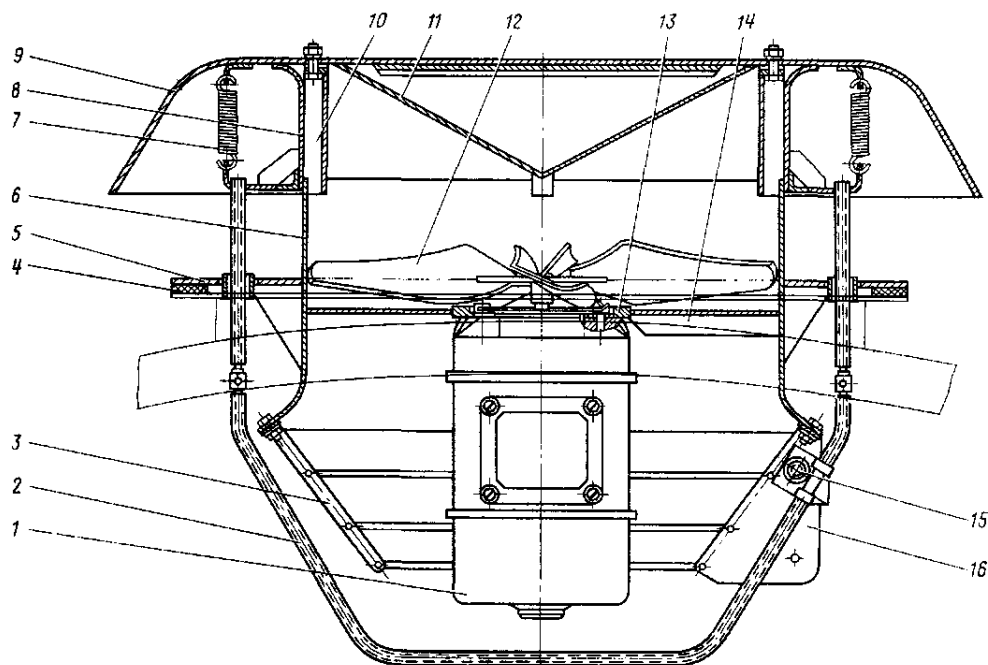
Вентилятор кузова: 1 - электродвигатель; 2 - тяга; 3 - сетка; 4 - прокладка; 5, 13 - фланцы; 6 - диффузор; 7- пружина; 8 - обечайка; 9-крышка; 10, 14 - угольники; 11- конус; 12-колесо вентилятора; 15 - фиксатор; 16- ребро сетки
